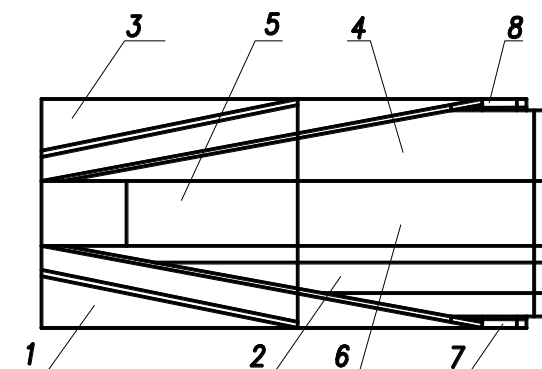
Схема инструмента ПКП для прокатки поковки «Палец цилиндра»
